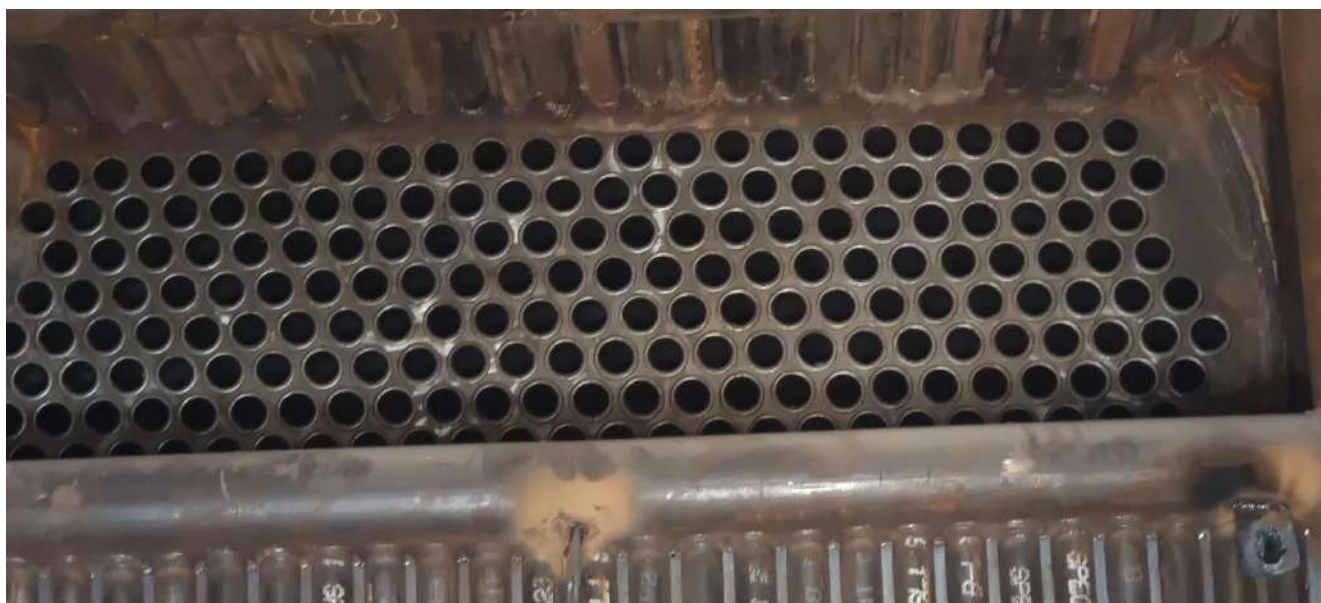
FORNALHA (ACESSO AO ESPELHO DIANTEIRO)
